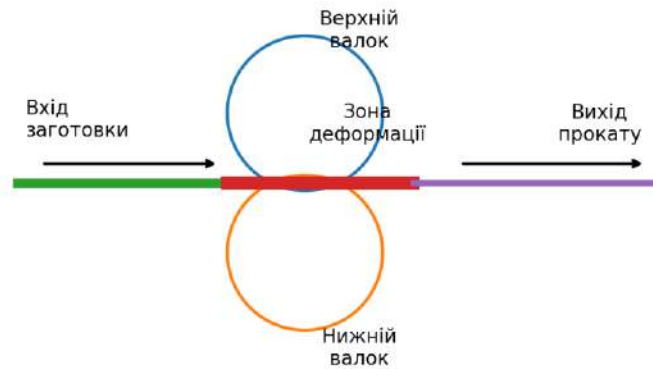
Узагальнена схема гарячого прокатування (вхід заготовки, осередок деформації, вихід металу)
